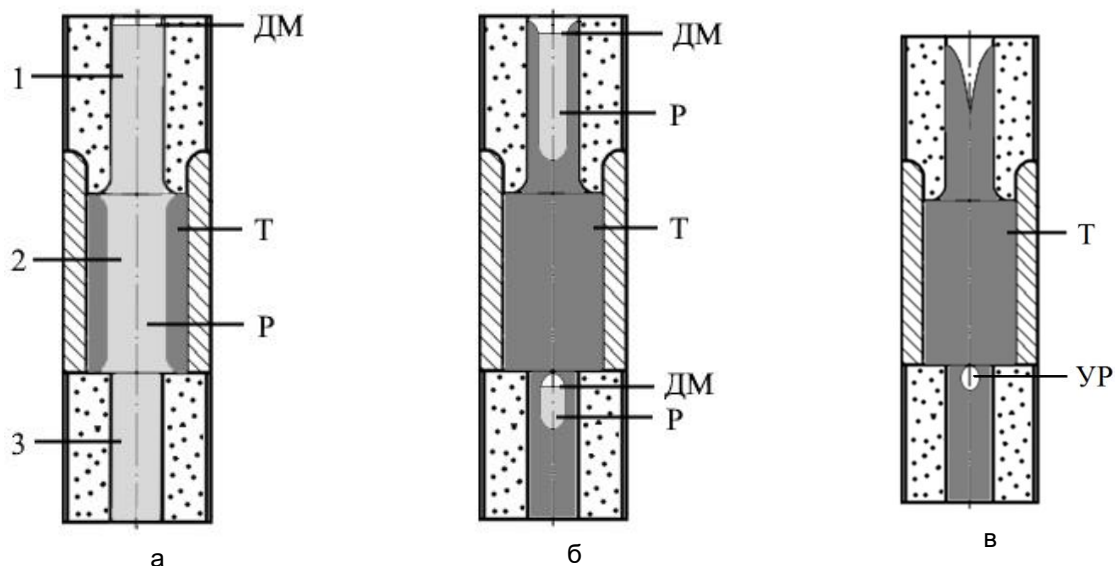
Схеми етапів виникнення усадкової раковини закритого типу в нижній шийці сортопрокатного валка: 1 – верхня шийка валка; 2 – бочка валка; 3 – нижня шийка валка; ДМ – дзеркало металу; Р – розплав; Т – тверда фаза; УР – усадкова раковина; а – вихідний стан; б – утворення термічних вузлів; в – утворення усадкової раковини
